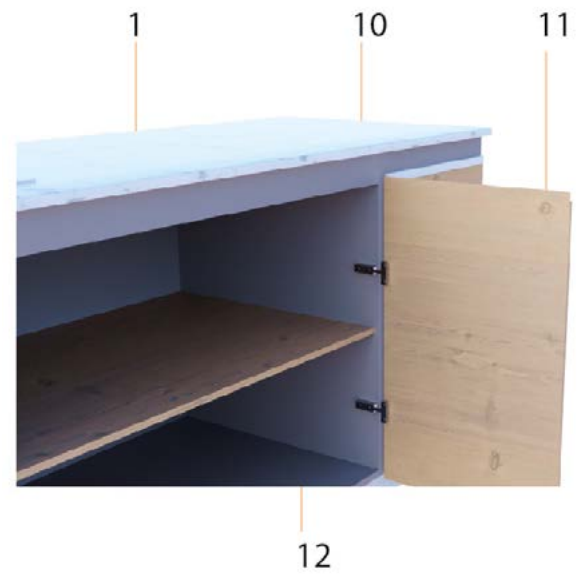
Detalle constructivo 3d mueble de cocina con madera de pino
